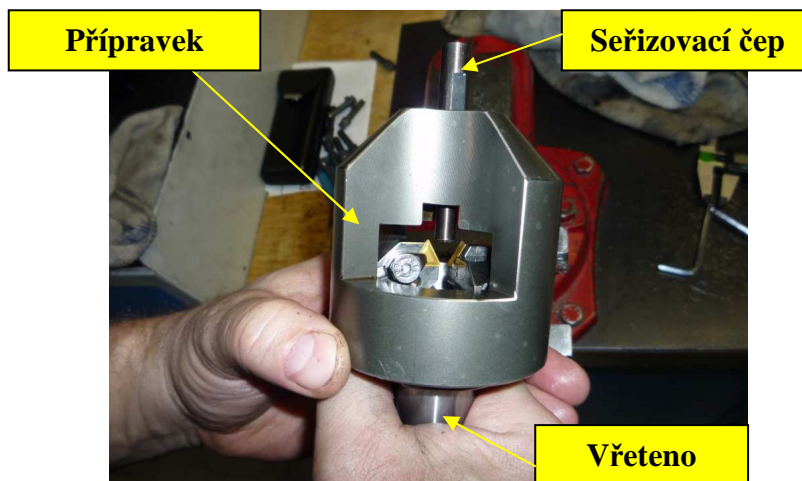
Demontáž břitových destiček z vřetena, které je upnuté ve svěráku
